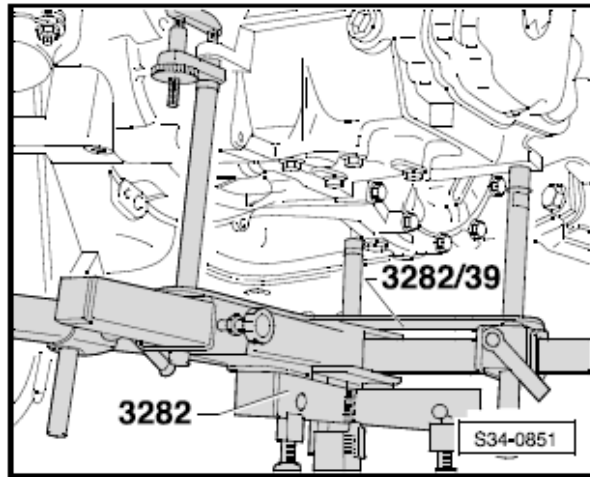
Приспособлення для кріплення коробки передач 3282
